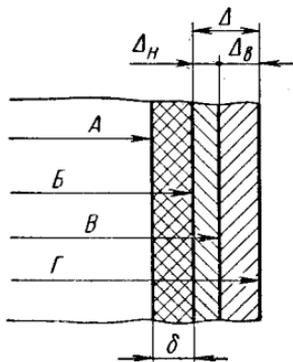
Схема размеров поковки с припуском и допуском
